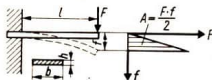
Skizze zur Berechnung einer Blattfeder
